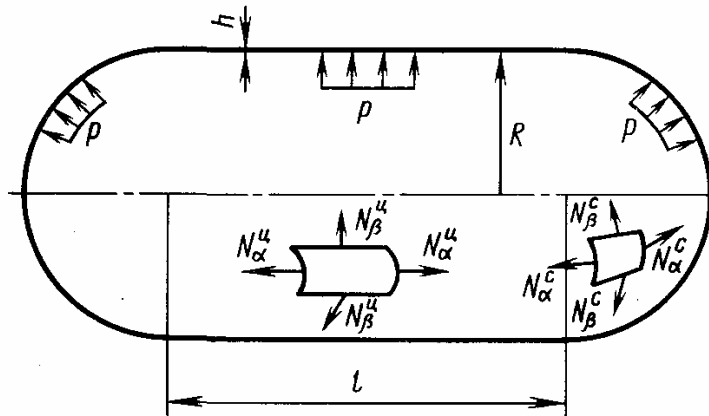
Цилиндрический баллон давления с полусферическими днищами
